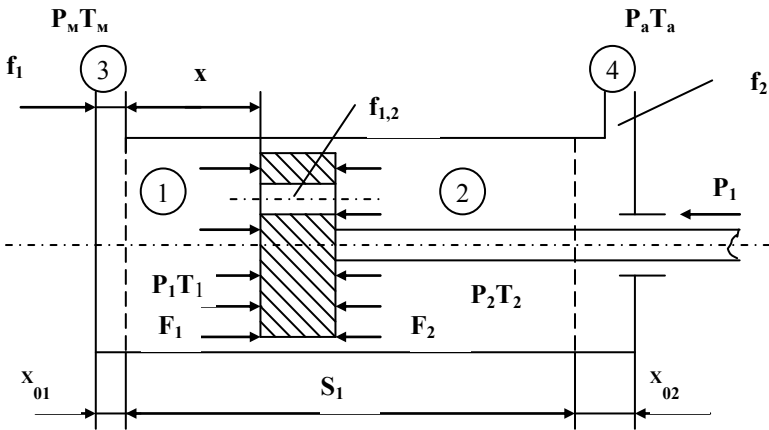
Схема пневматичного циліндра з внутрішніми втратами
